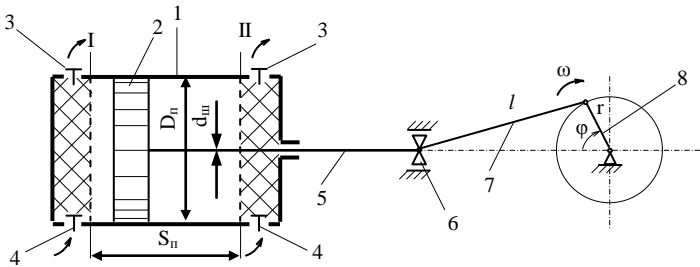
Схема поршневого компрессора с цилиндром двойного действия.
